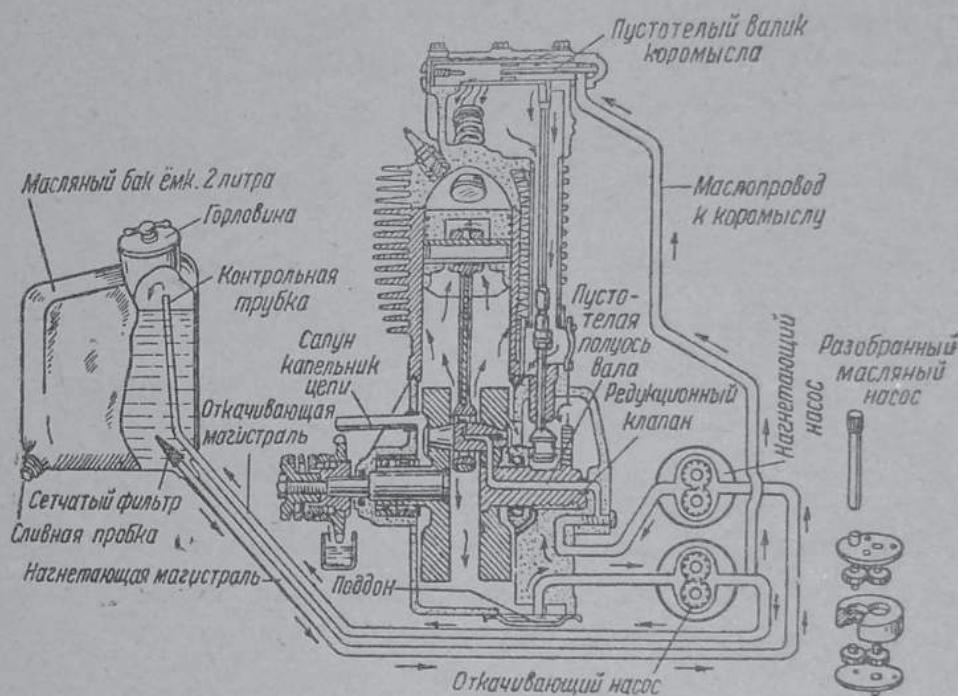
Схема смазки двигателя Харлей-Дэвидсон.
